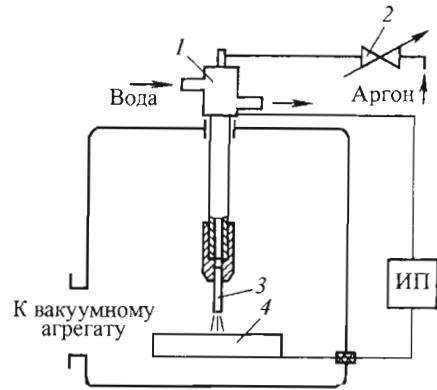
Схема сварки полым неплавящимся катодом в вакууме:
